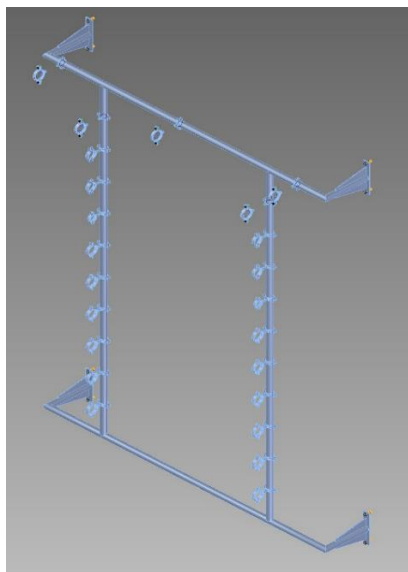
Strutture a sostegno delle tubazioni sulla parete sud (Solid Edge)
